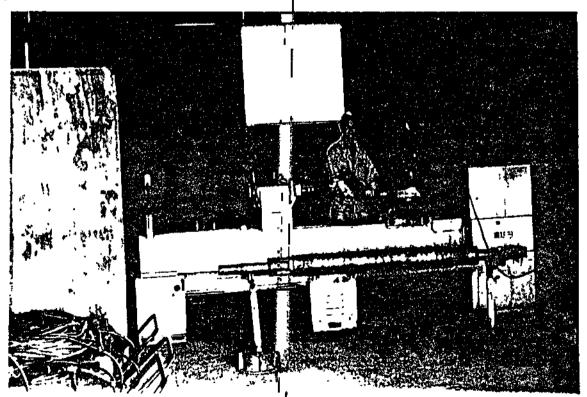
Detailes da infraestrutura. Na foto o torno instalado na oficina e para dar apoio aos trabalhos de mecânica.
